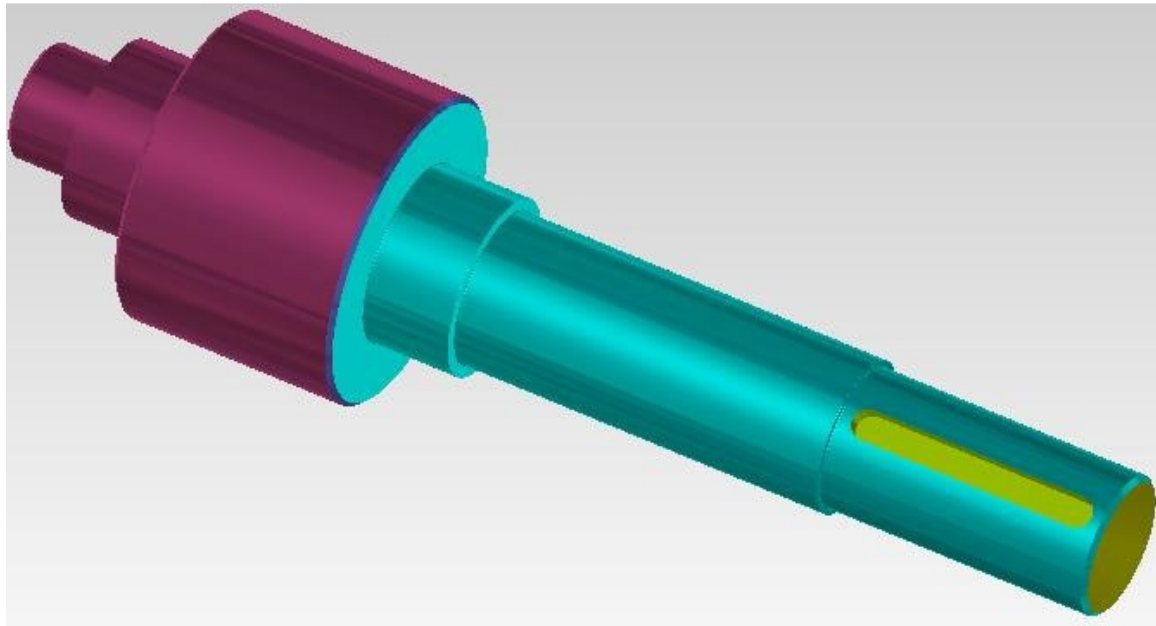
Тривимірна модель деталі після токарної обробки
